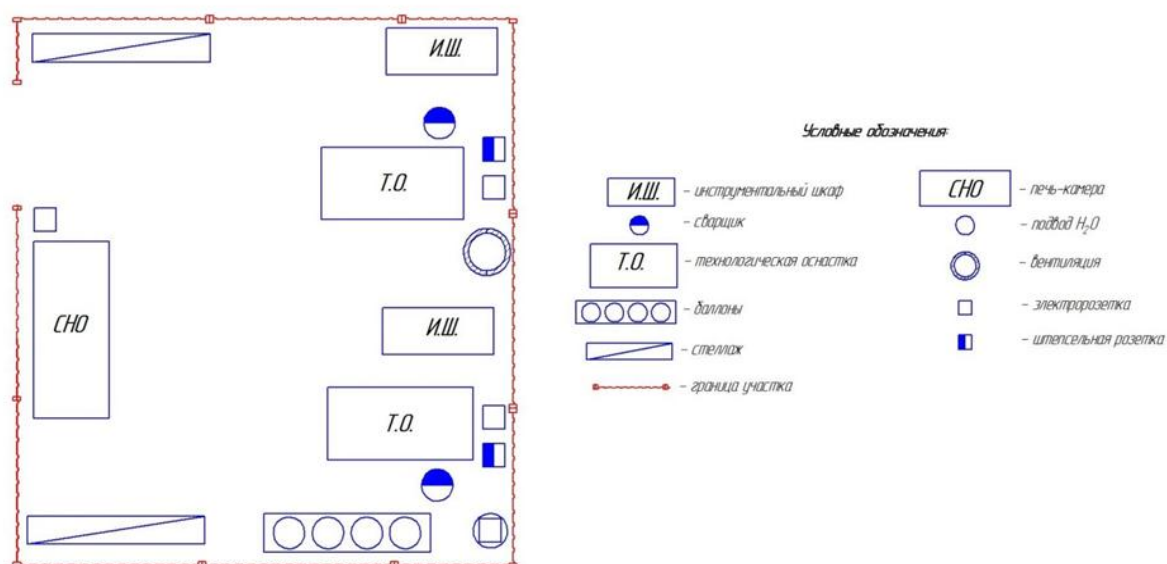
Сварочный участок для восстановления шнека экструдера
